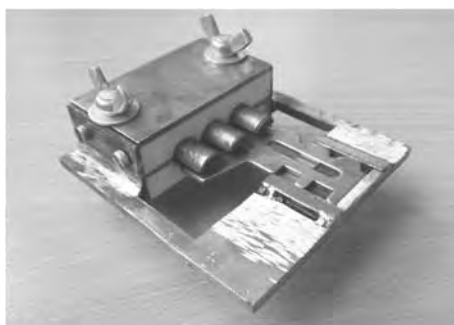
Приспособление для сборки и сварки засова
